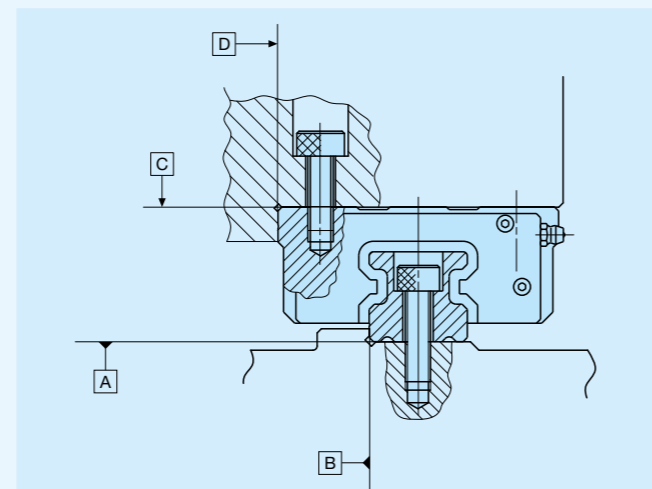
Superfície de montagem de referência e estrutura de montagem típica
